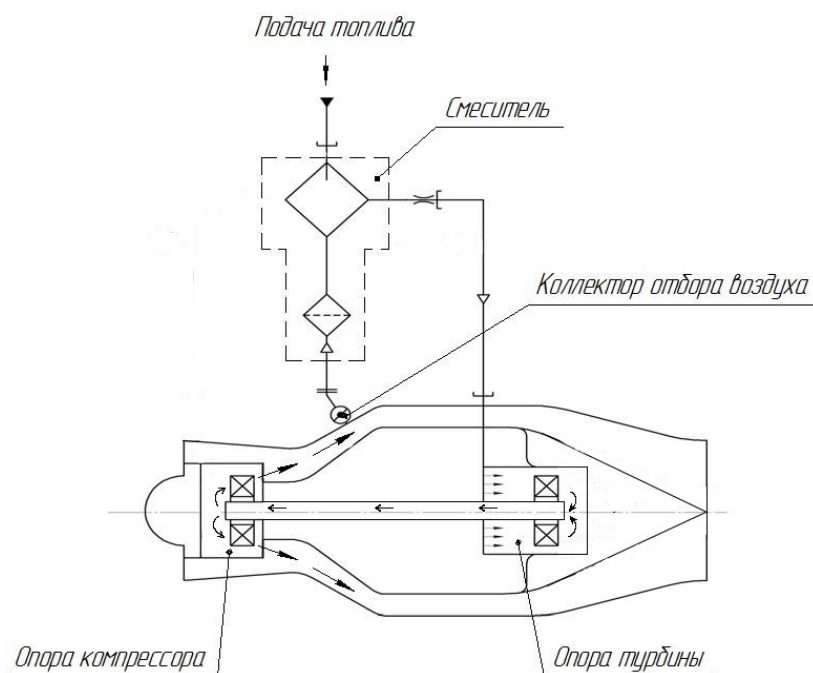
Схема смазки и охлаждения роторных подшипников ГТД воздушно-топливной смесью
